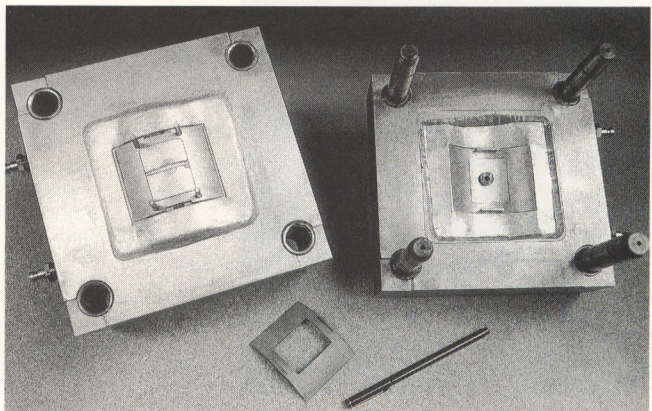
Metallgespritztes Spritzgießwerkzeug für ein elektrisches Schaltelement aus Polycarbonat
